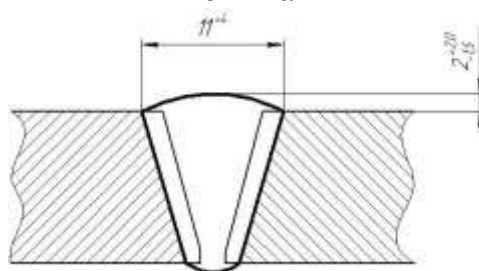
Размеры сварного шва при соединении труб диаметром 325 мм толщиной стенки 12 мм
